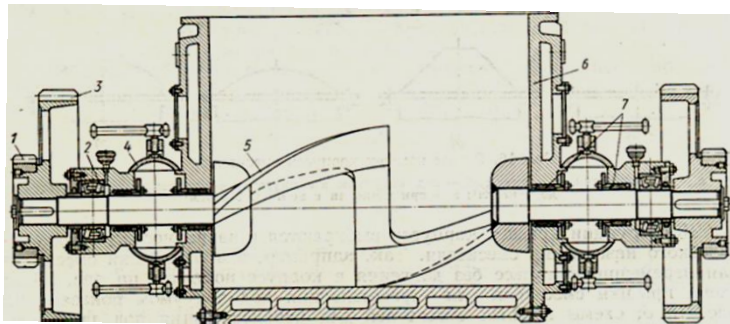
Лопатевий вал з Z-подібними лопатями змішувача на 800 літрів: 1,3 – зубчасті колеса; 2 – підшипник; 4 – сальникова коробка; 5 – лопатевий вал; 6 – бокова стінка; 7 – сальникове ущільнення
